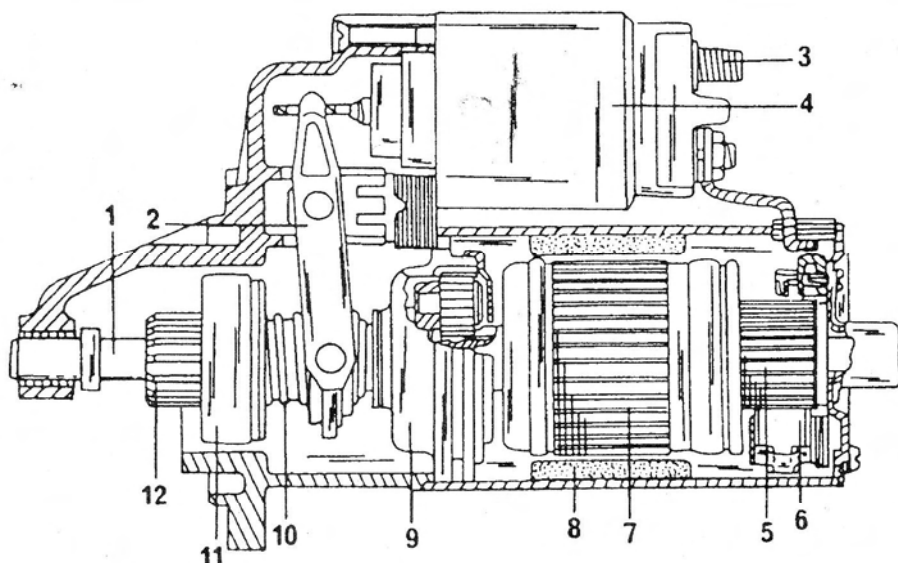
Разрез стартера с принудительным включением и самовыключением шестерни Bosch.
